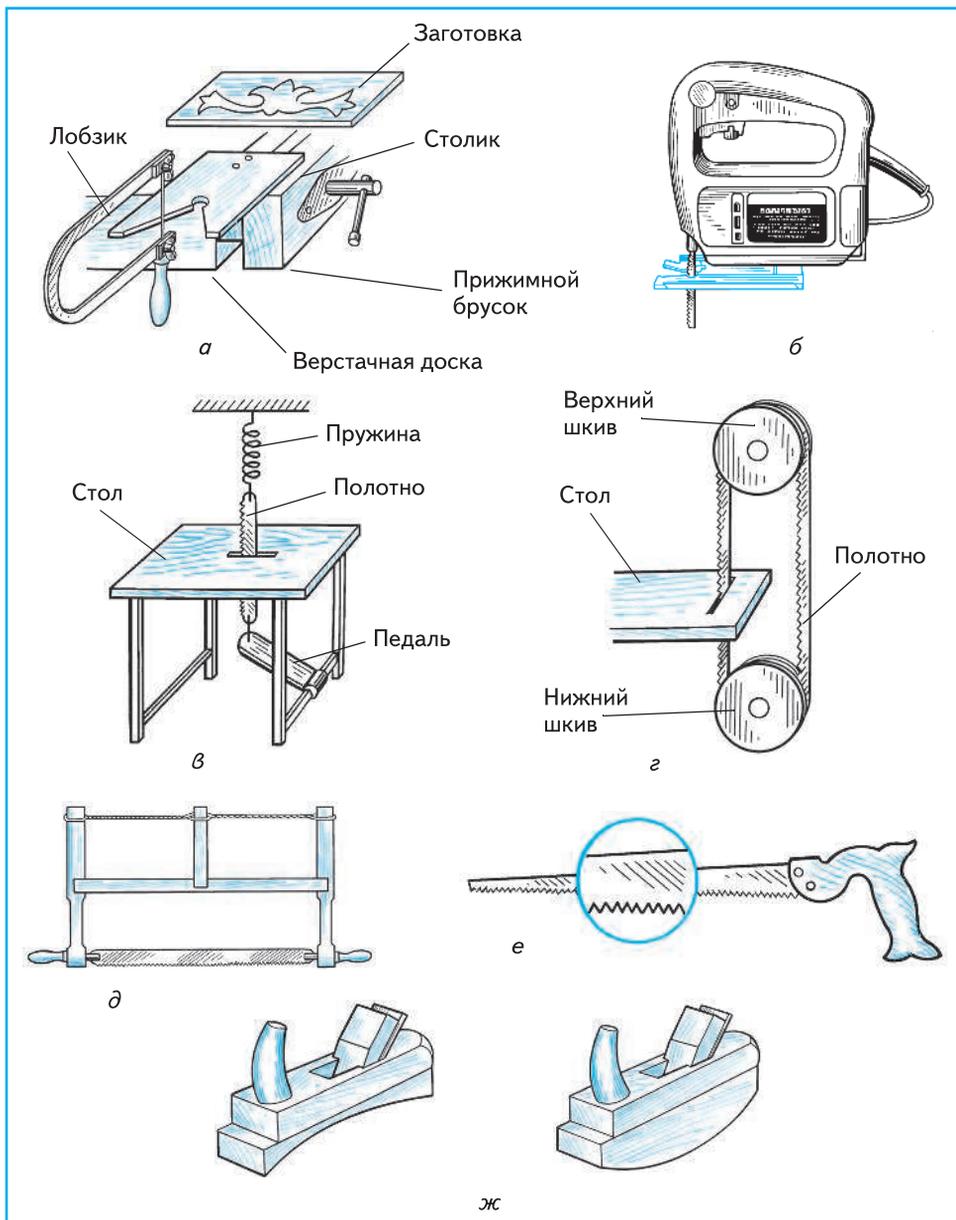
Инструменты и приспособления для изготовления плоских изделий криволинейной формы: *а* — организация рабочего места для выпиливания лобзиком; *б* — электрический лобзик; *в* — ножной лобзик; *г* — ленточный станок; *д* — выкружная лучковая пила; *е* — курковка; *ж* — горбачи
